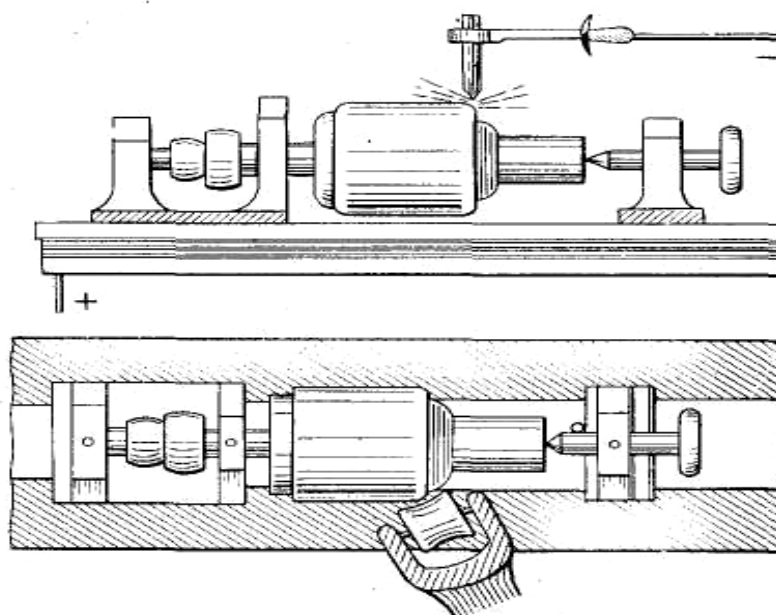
Устройство для сварки продольных швов листов, труб и цилиндров большого диаметра
